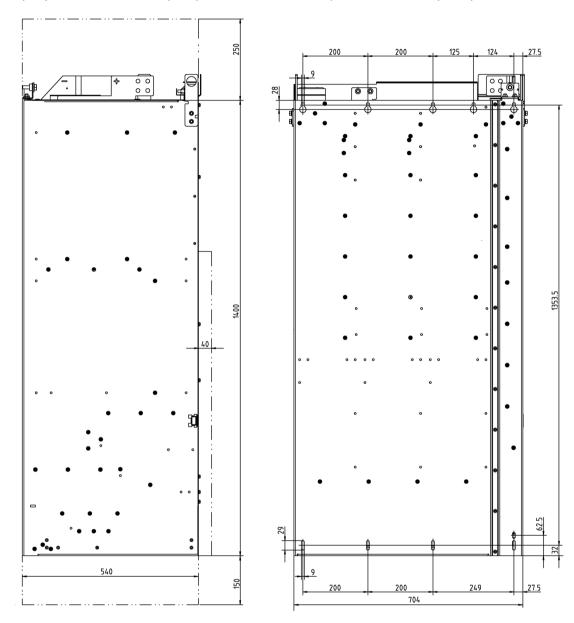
Габаритный чертеж модуля двигателя, типоразмер ЈХ. Вид сбоку, вид сзади
